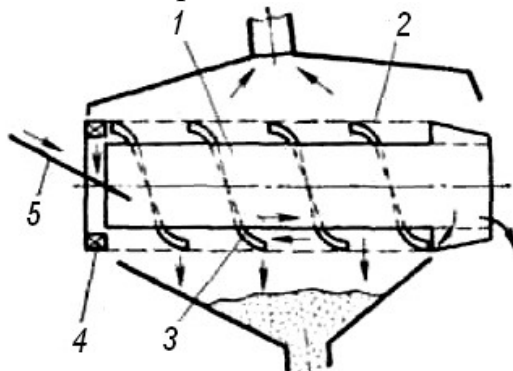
Галтовочный барабан непрерывного действия для очистки отливок
